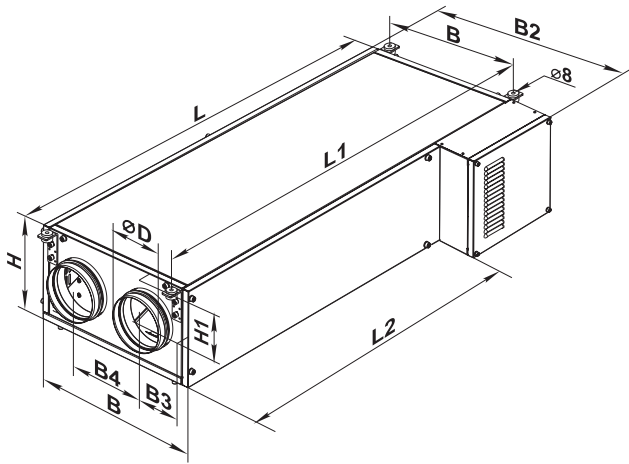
Габаритні розміри установки ВУТ 350 ПЕ ЕС
